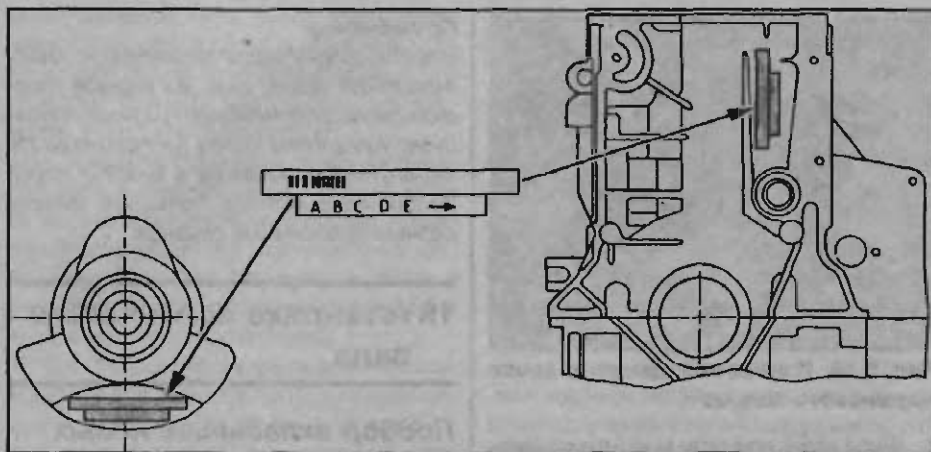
Расположение меток на блоке цилиндров и коленчатом валу двигателя 1,6 л для выбора коренных подшипников коленчатого вала
